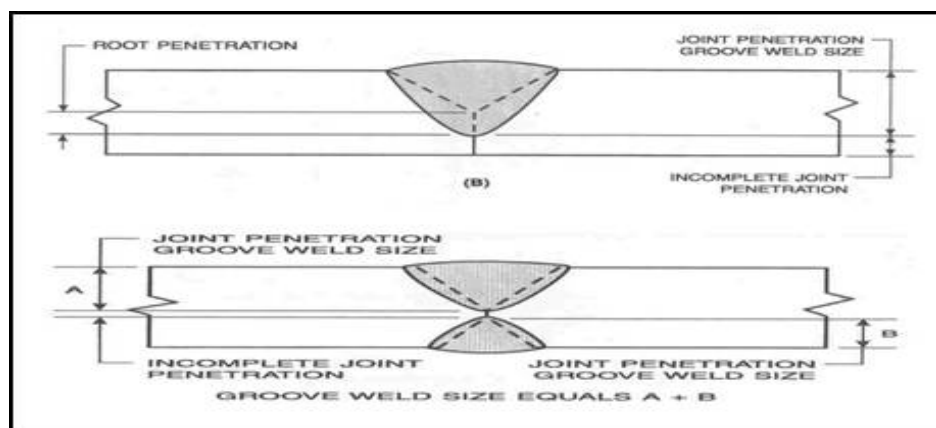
Partes de la junta soldada. Fuente Instituto chileno de soldadura. Página 24.
